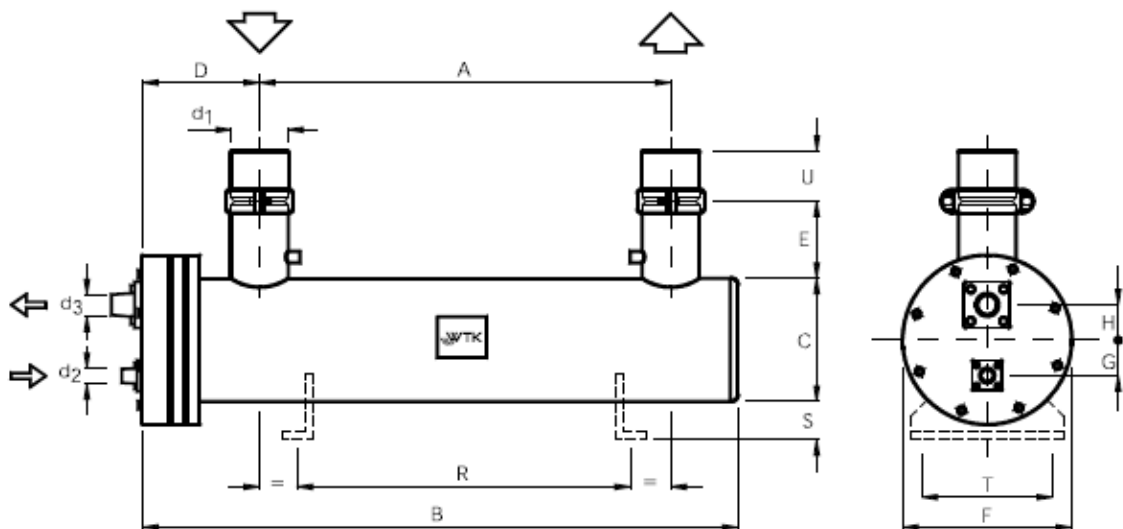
Схема випарника WTK SCE 393 з габаритними розмірами
